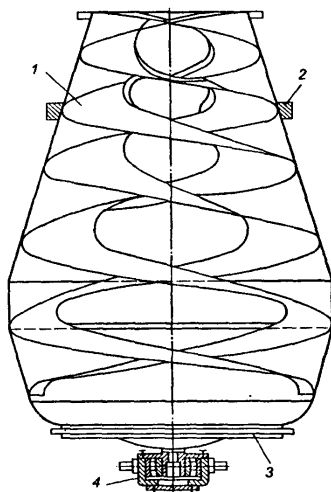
Смесительный барабан: 1 – лопасти; 2 – бандаж; 3 – зубчатый венец; 4 – подшипник
